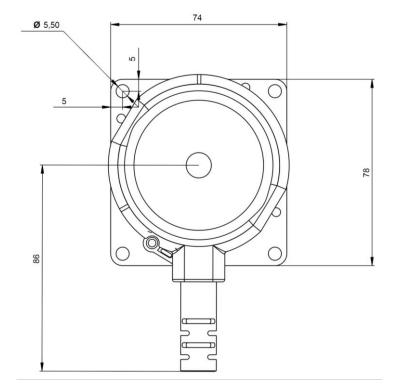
Установочные размеры. ДУТ – вид сверху
